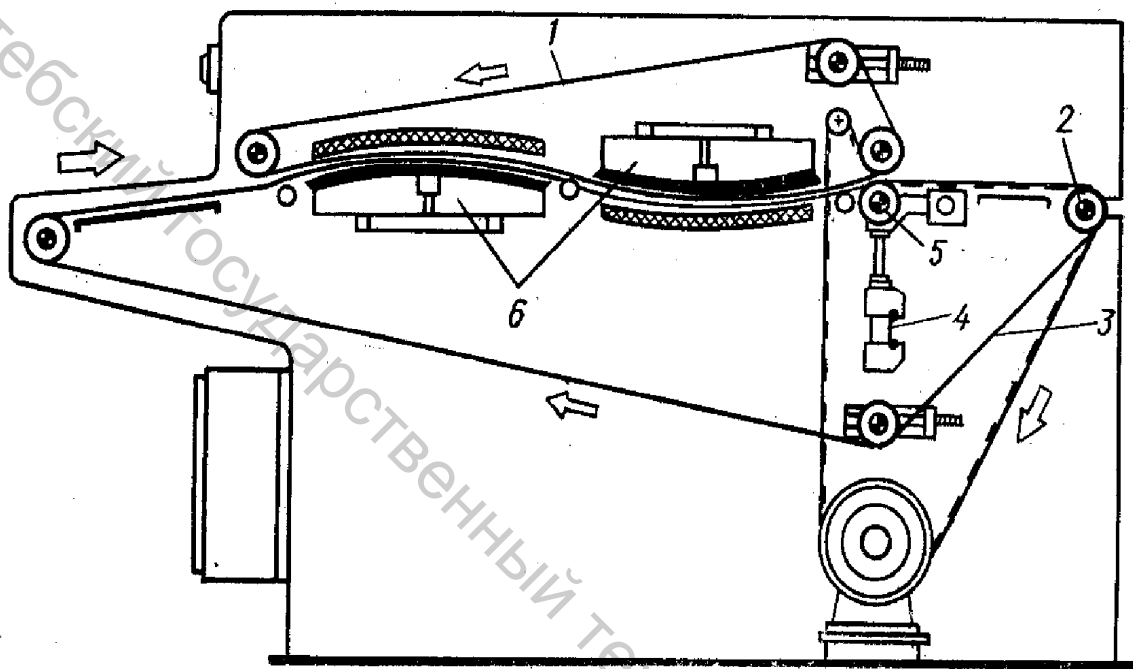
Схема работы прессы “Mini-Mac” для объемного формования деталей
